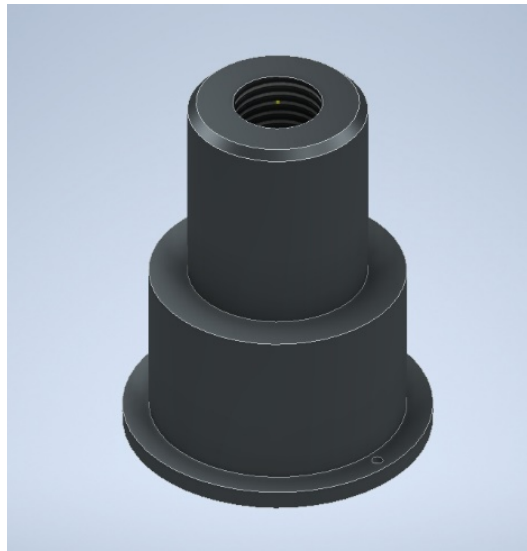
Perspectiva axonométrica de la tuerca del husillo.
